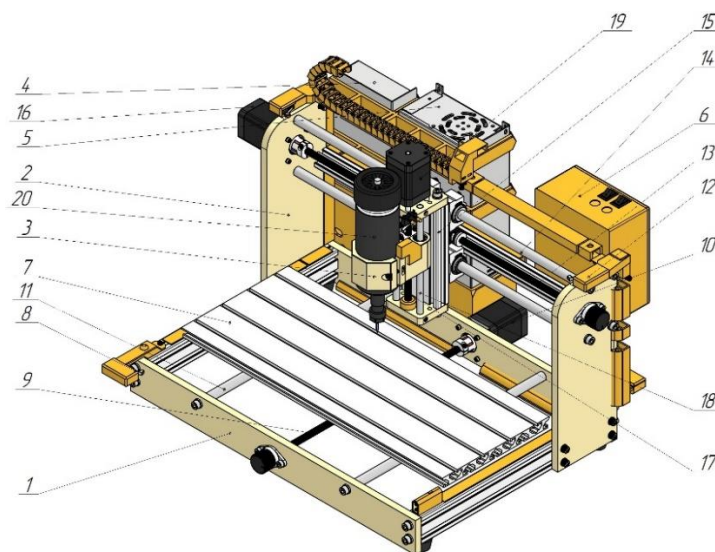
Фрезерно-гравірувальний верстат з ЧПК (CNC 3018-Plus)
